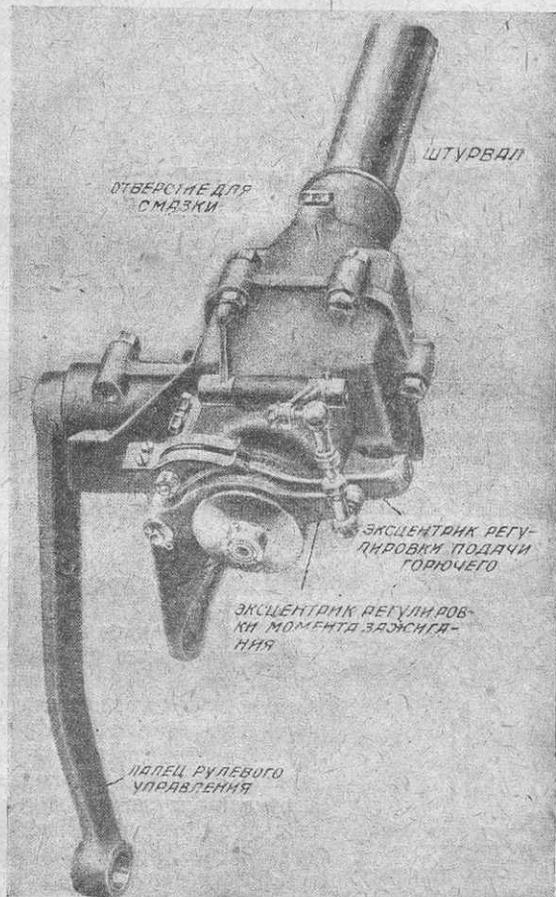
Коробка рулевого механизма и палец (сошка) рулевого управления.
